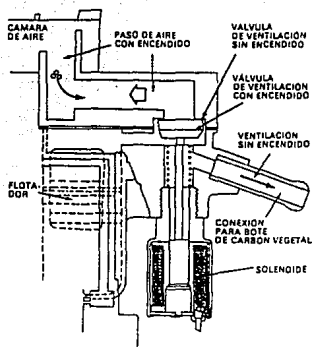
Vista en sección de un carburador en que se muestra el respiradero controlado por solenoide del bote de carbón
